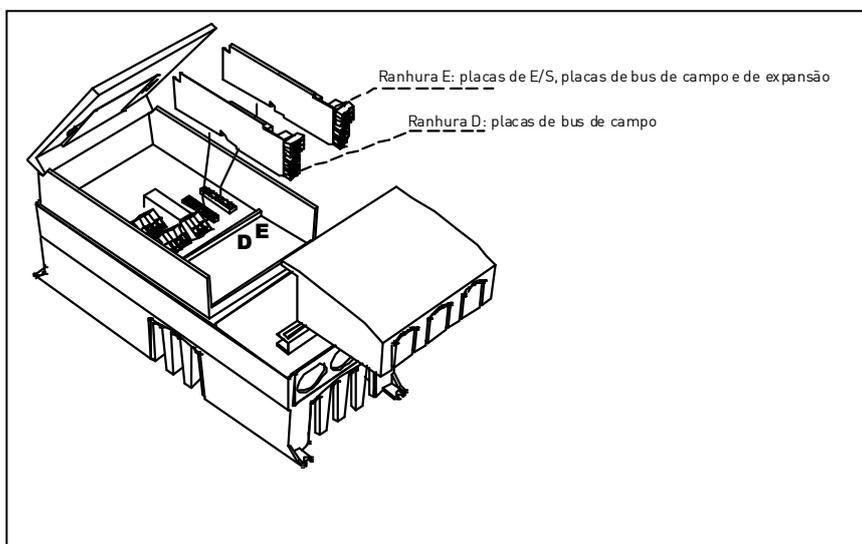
Ranhuras D e E para placas opcionais nas estruturas MF4 – MF6
